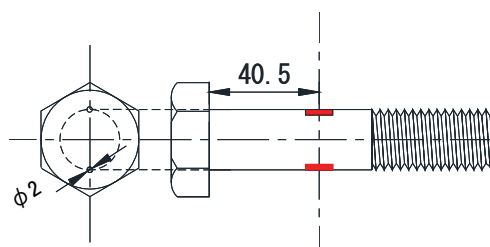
ボルト軸部のひずみゲージ貼付位置 (単位 : mm)
